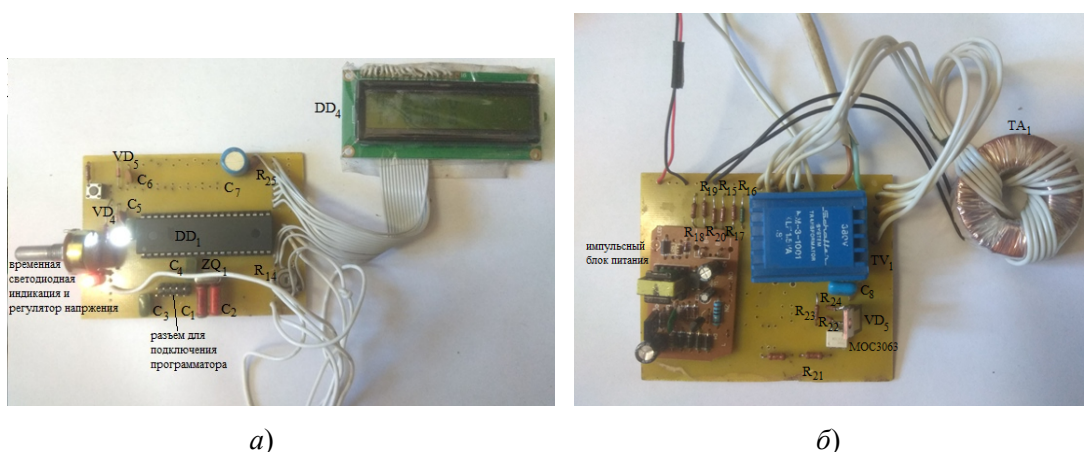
Внешний печатный плат макета микропроцессорного автоматического выключателя
